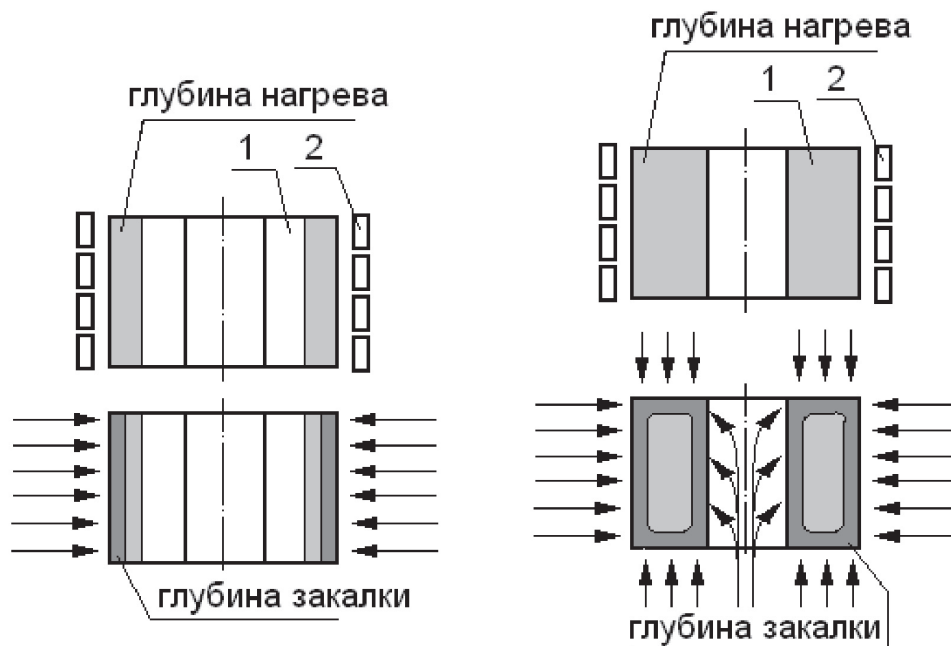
Схема контурного объемно-поверхностного упрочнения изделия из стали ПП
